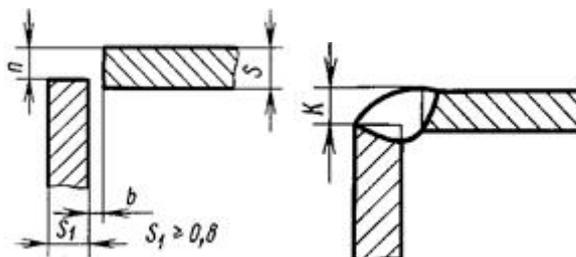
Типы сварного соединения У4 ГОСТ 14771 – 76
